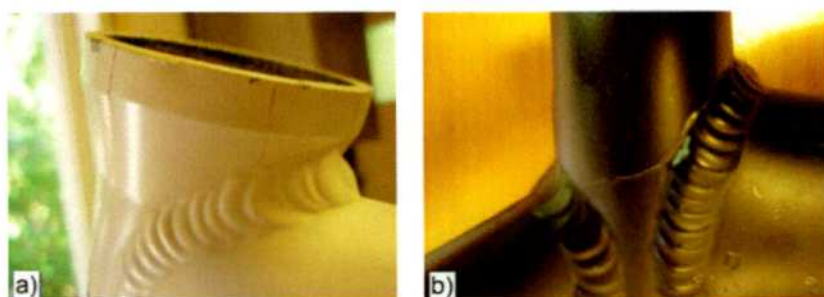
Cuadro 3. a) Zona del tubo frontal donde calza el stem. b) Zona del tubo soporte del sillín
